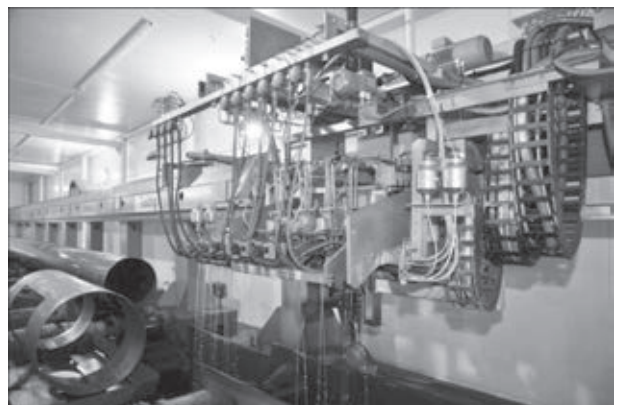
Установка для ультразвукового контроля основного металла и сварного соединения трубы
